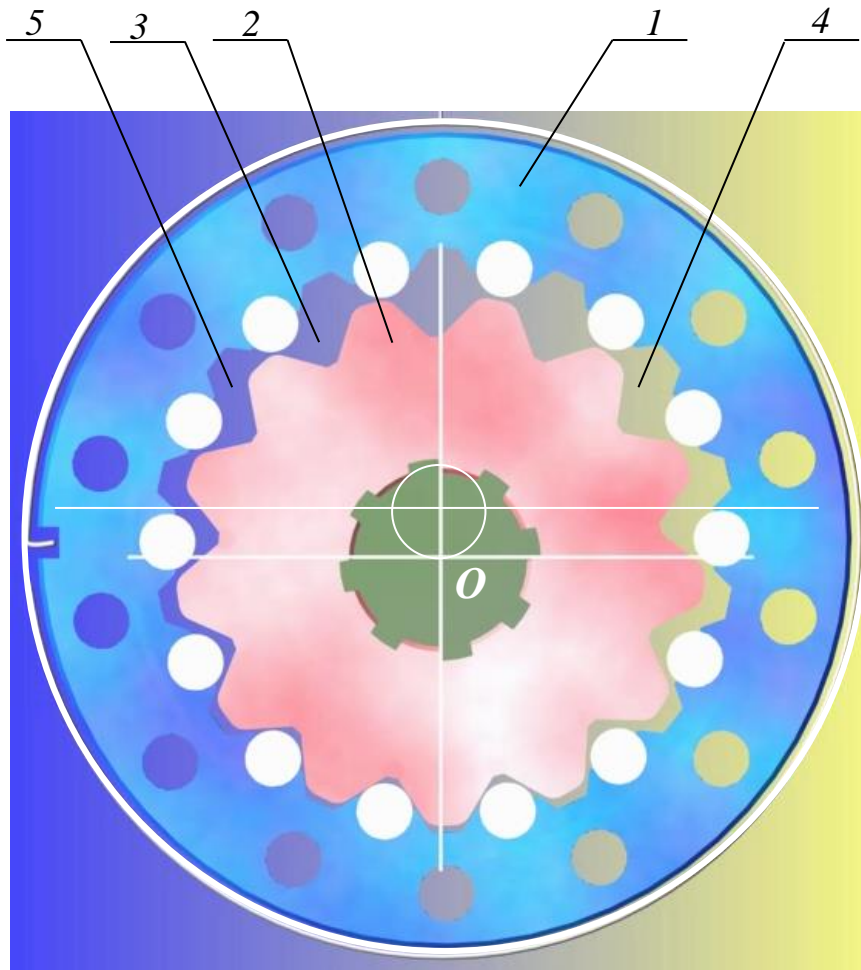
Зубчатая пара с внутренним гипоциклоидальным зацеплением: 1 – корпус (направляющая); 2 – ротор (шестерня); 3 – рабочие камеры; 4 – зона нагнетания; 5 – зона слива.
